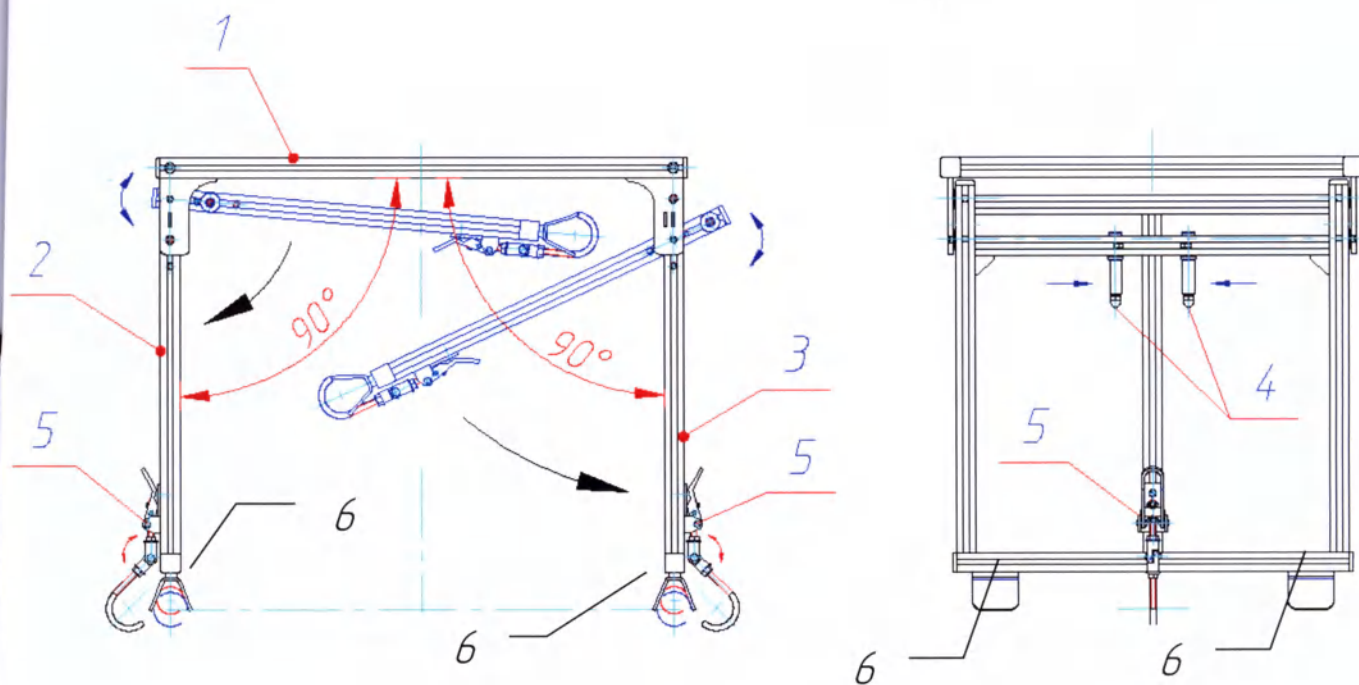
Порядок приведения полки для оборудования в рабочее (или транспортное) положение.
